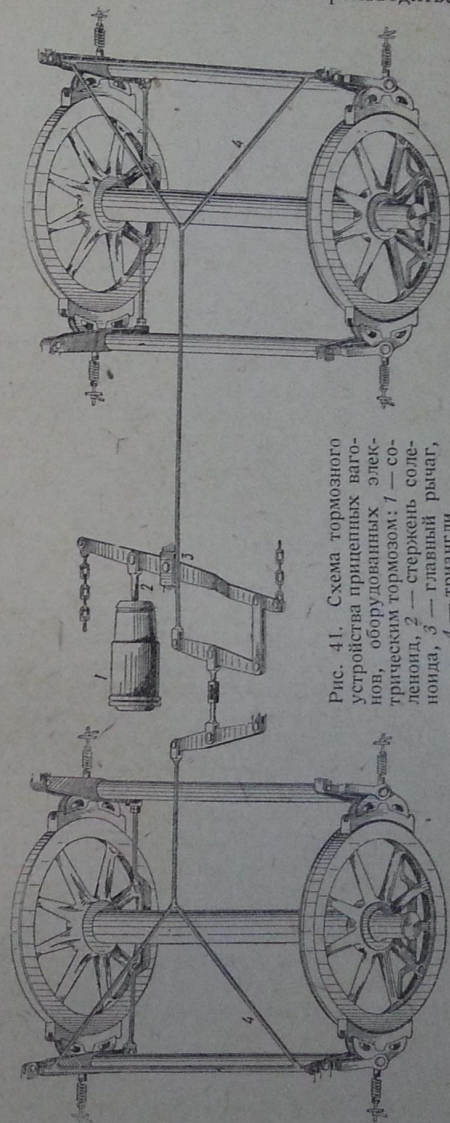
Схема тормозного устройства прицепных вагонов, оборудованных электрическим тормозом: 1 — соединитель, 2 — стержень соединитель, 3 — главный рычаг, 4 — триангли.
